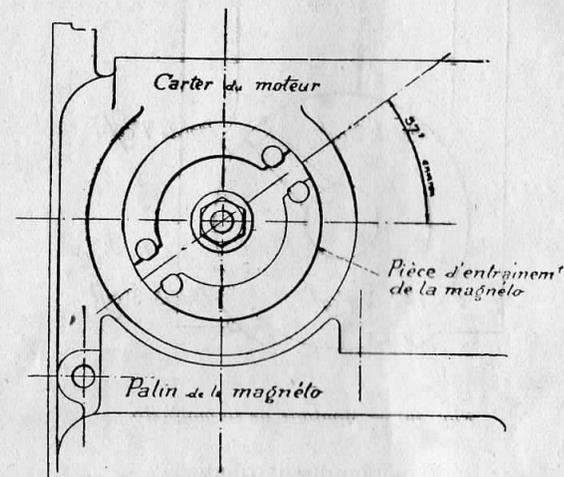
Position du cardan d'entraînement de la magnéto lorsque le piston du premier cylindre est au point mort haut fin de compression.
